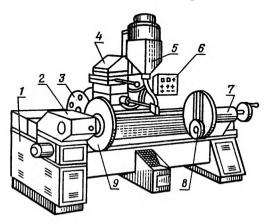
Станок У-652 для наплавки коленчатых валов:
